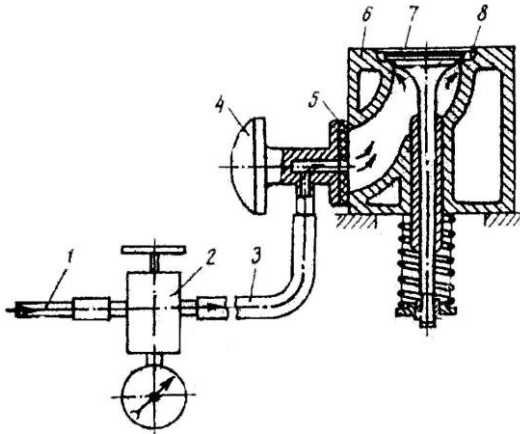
Пневматичне прилад для перевірки герметичності клапанів: 1 і 3- гнучкі повітропровода; 2- повітряний редуктор; 4- прижим; 5 - гумова прокладка; 6- головка циліндрів; 7- тарілка клапана; 8- гніздо клапана
